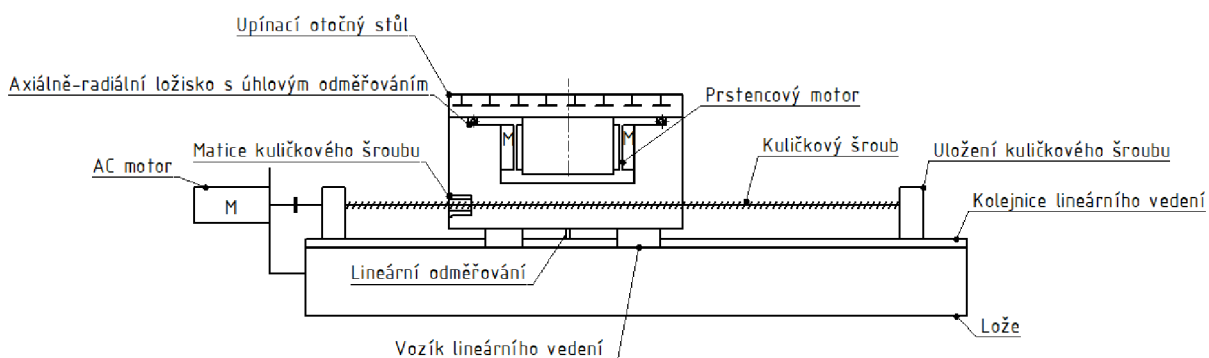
DRTB otočný stůl od firmy Demmeler [18]
